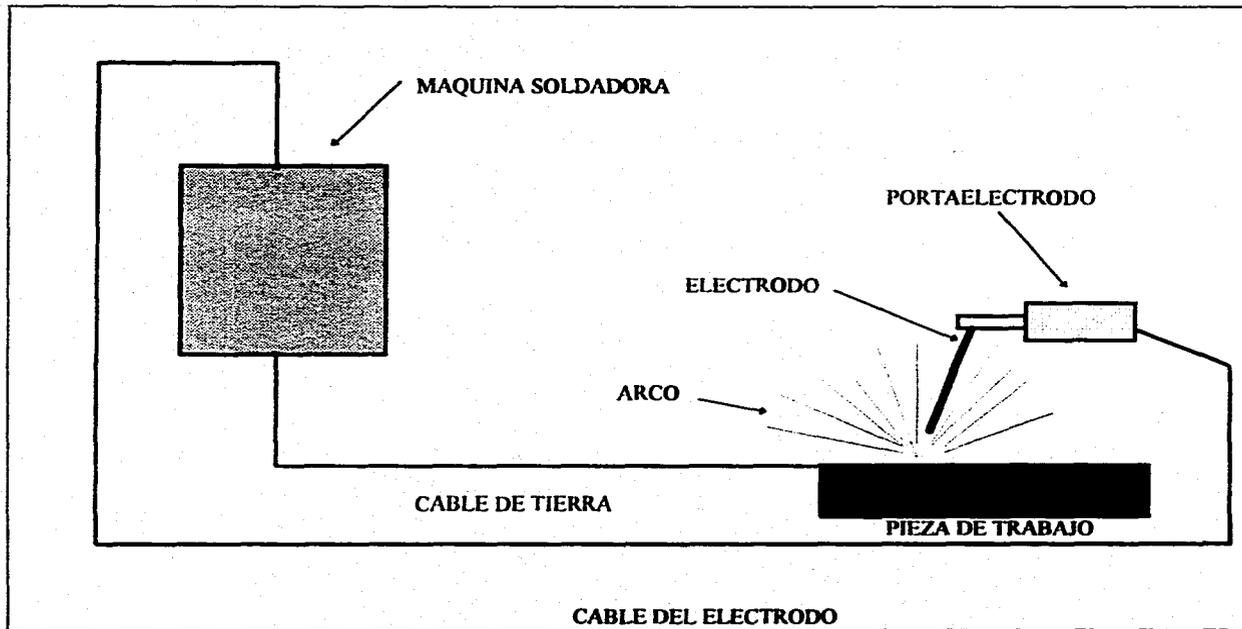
Circuito básico de soldadura eléctrica por arco
